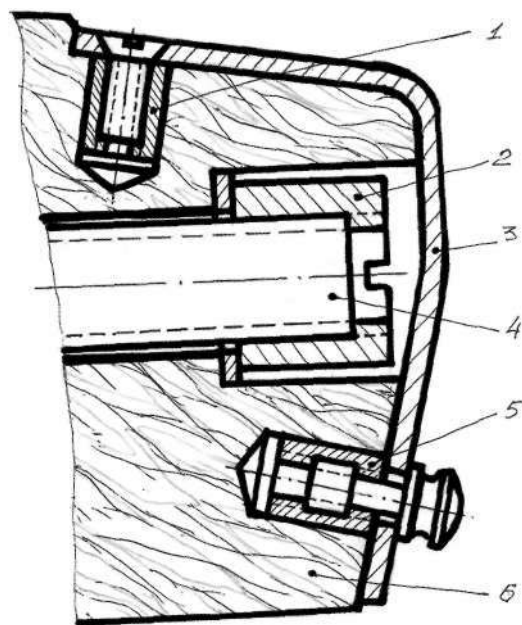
Схема крепления навершия охотничьего ножа «Стремительный»: 1,5 — гайки, запрессованные в дерево (см. рис. 5.23, работа над ножом «Абанат»); 2 — затяжная гайка; 3 — навершие; 4 — хвостовик ножа. 6 — черен
